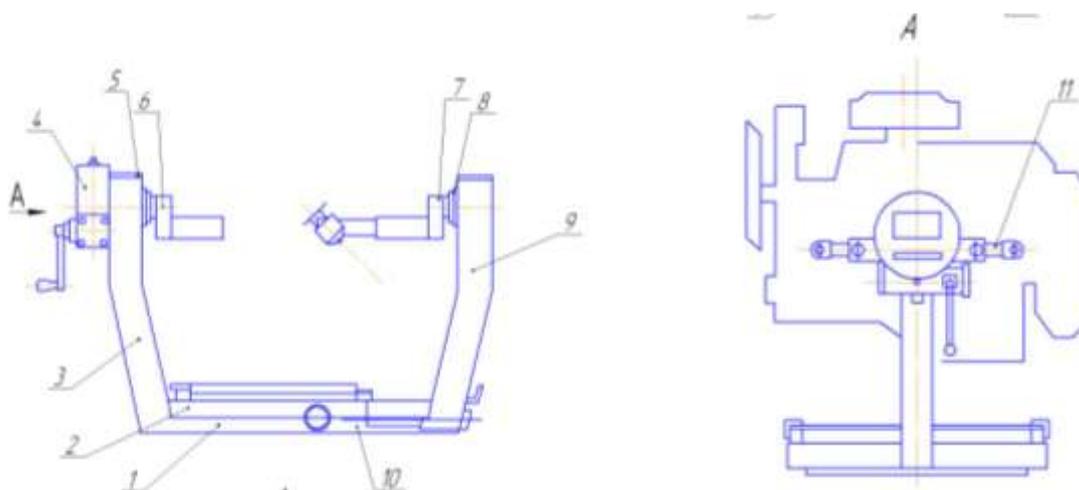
Стенд для разборки и сборки двигателей (модель С 152)
